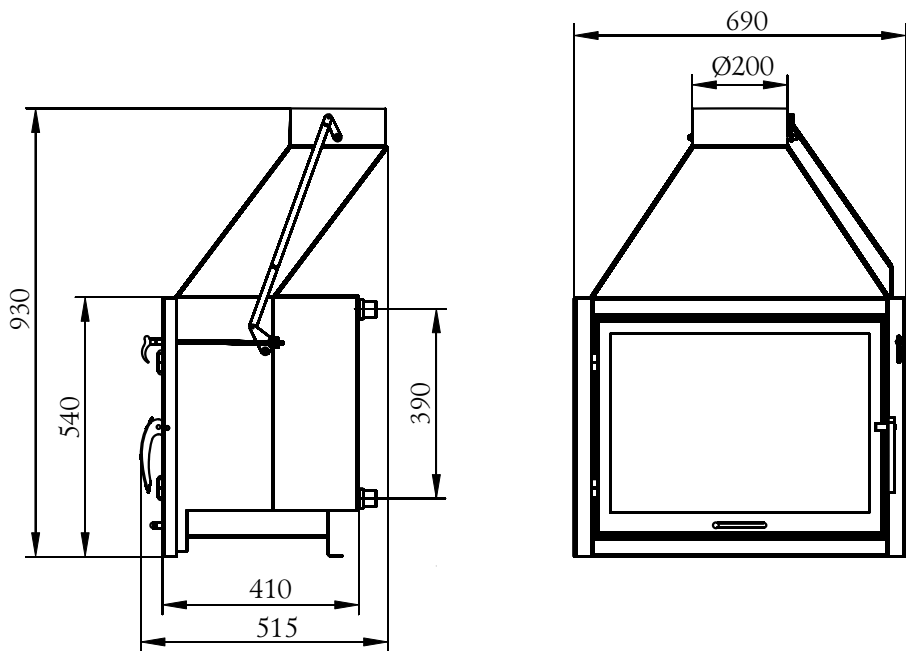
Габаритные размеры каминной топки «Аквариус».
